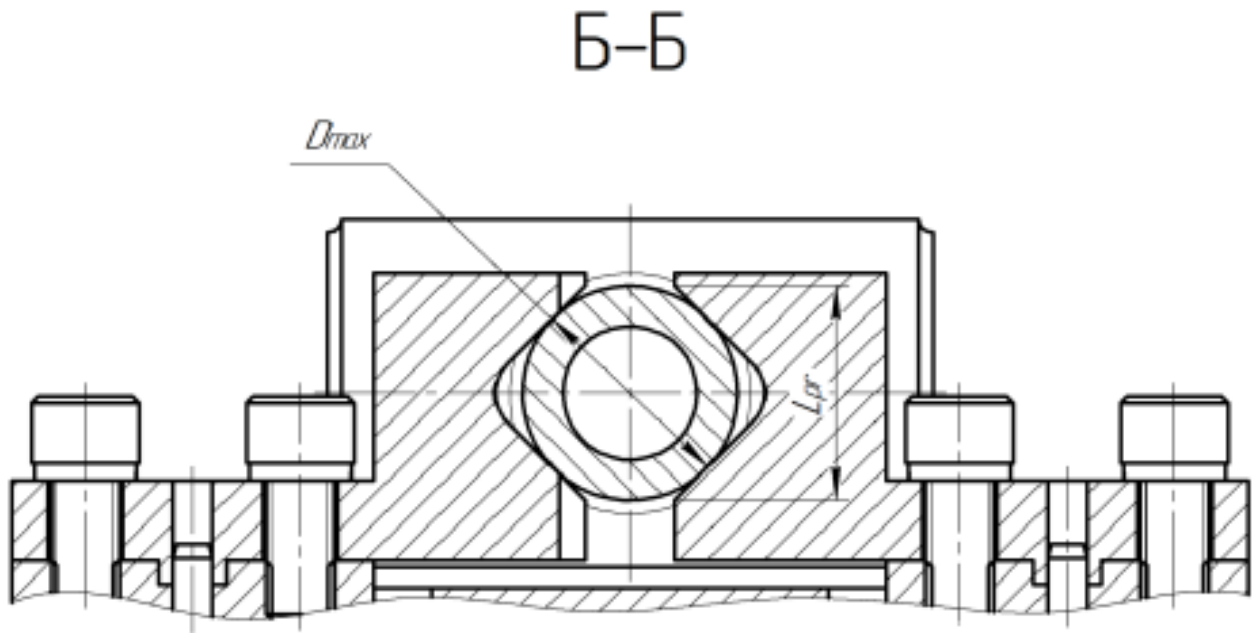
Граничні габаритні розміри деталей, які можливо затискати даним верстатним пристроєм, для оброблення деталей типу вилок максимальних розмірів, розріз Б-Б [201]
